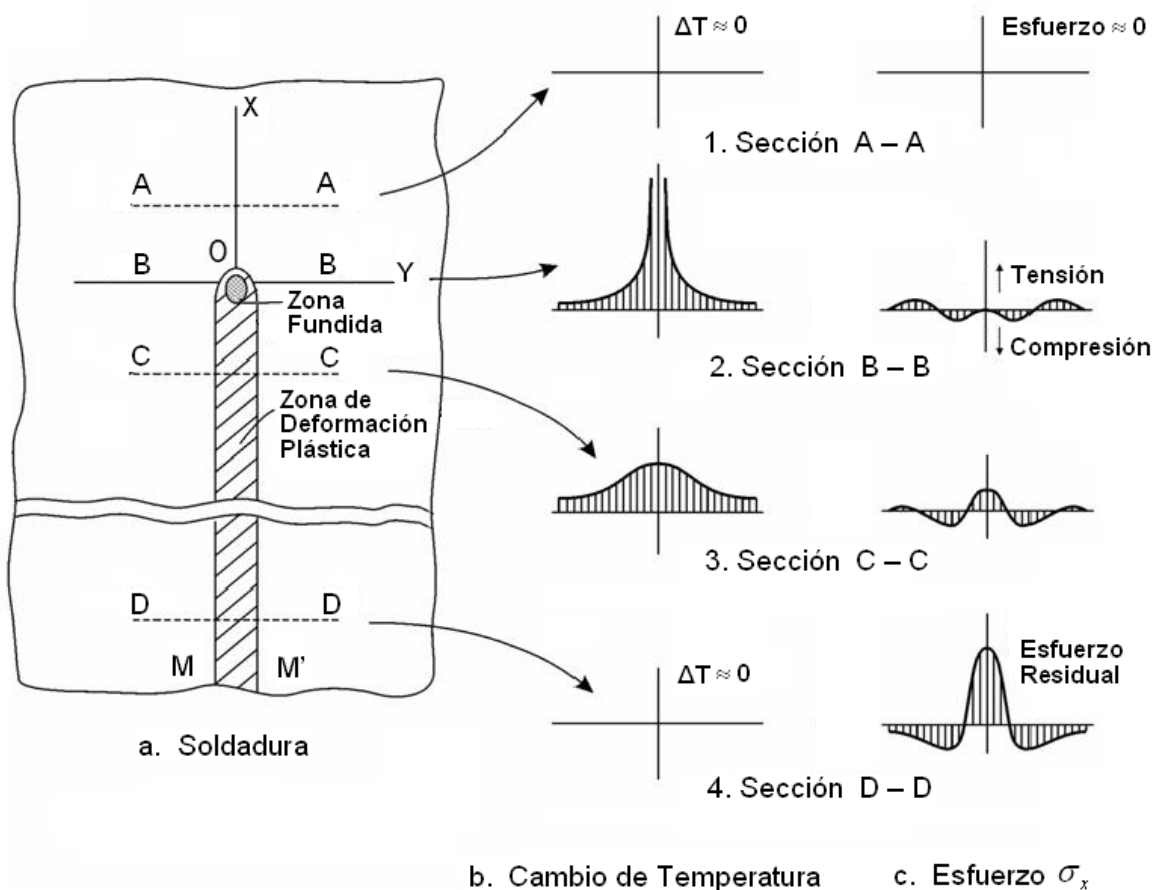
Cambio de temperatura y de esfuerzos durante la soldadura⁹
